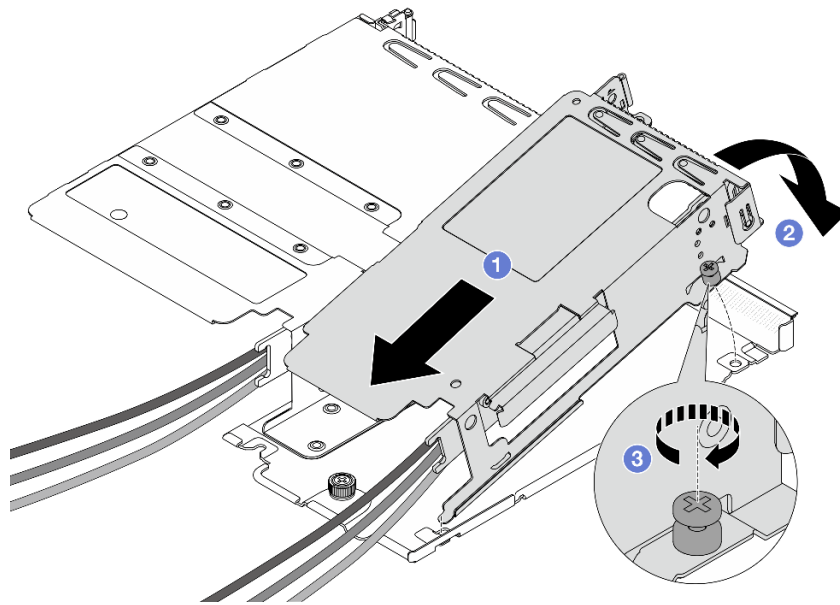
Assemblage des deux boîtiers de cartes mezzanines
